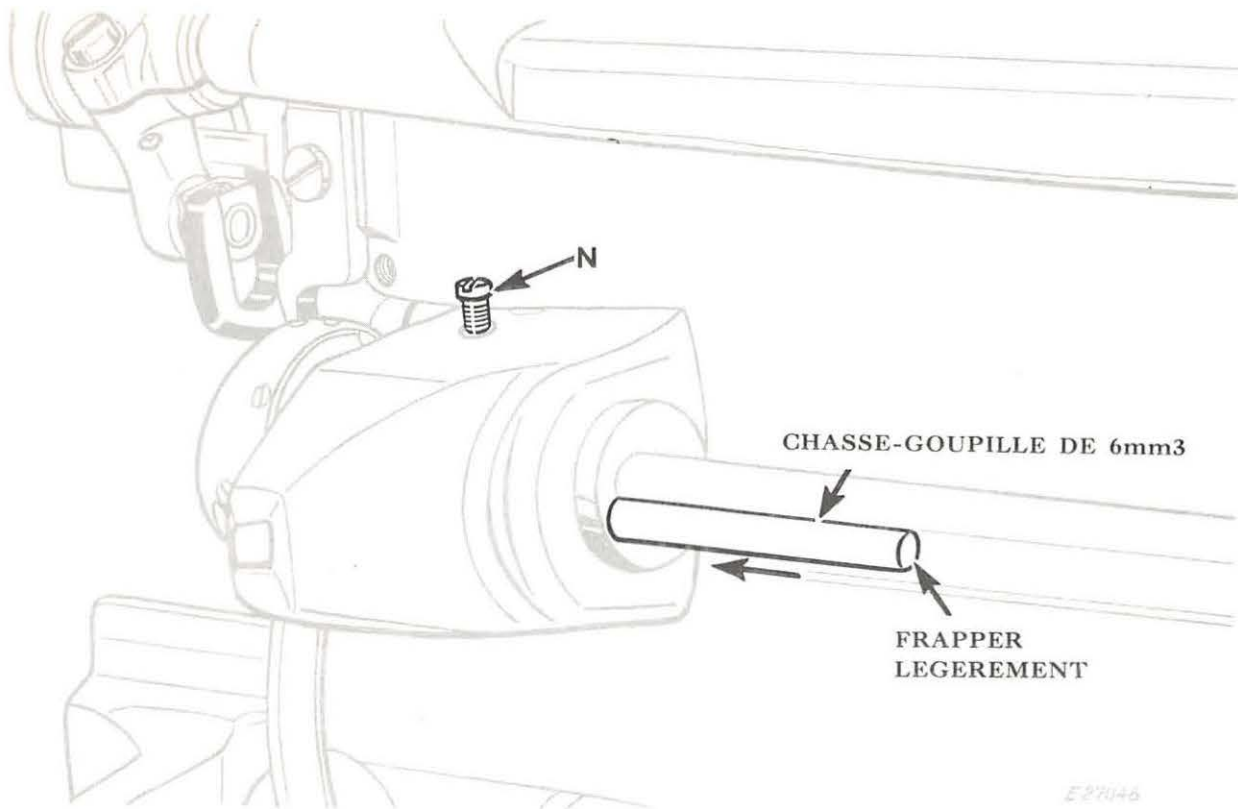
Assemblage de crochet chassé en DIRECTION de l'aiguille
